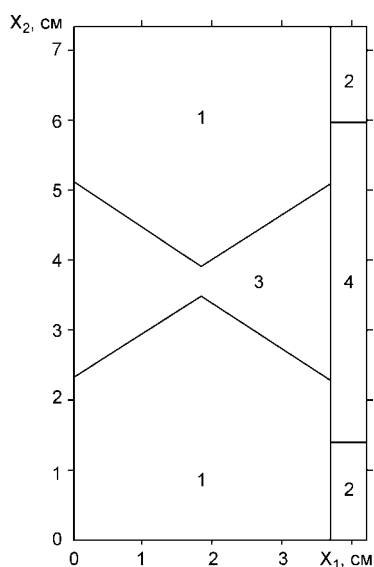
Схема сварного соединения: материал основы (1), плакирующий слой (2), сварной шов основы (3), сварной шов плакирующего слоя (4)
